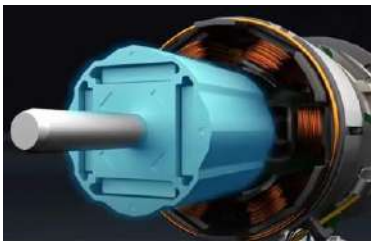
Бесщёточный двигатель с инкорпорированными магнитами в сердечник ротора
